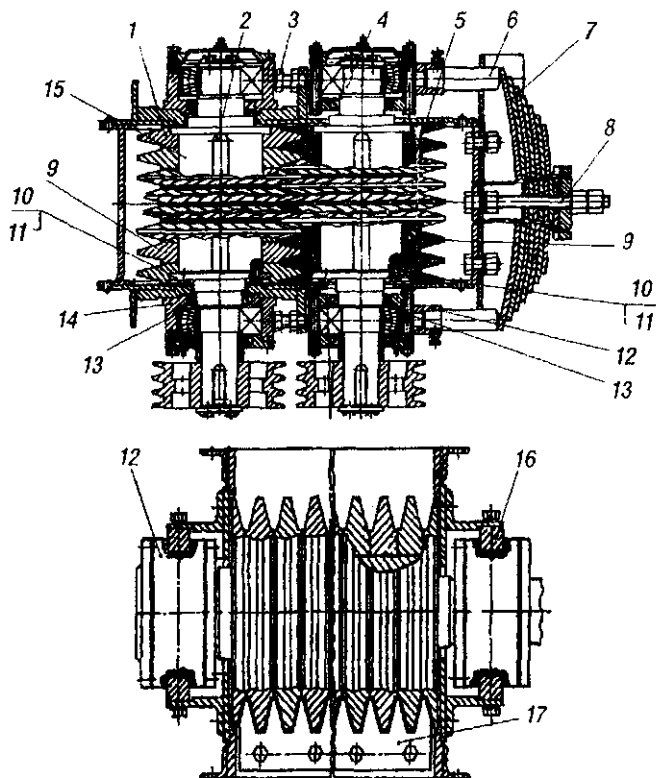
Схема рабочей камеры вальцово-дисковой плющилки
